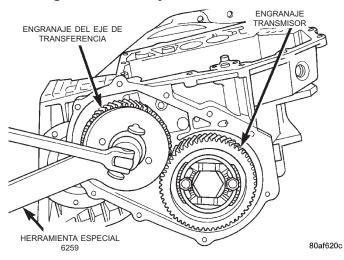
Desmontaje de la tuerca del engranaje del eje de transferencia
